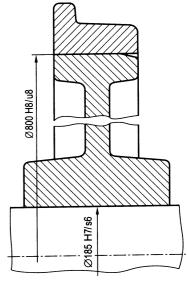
Крепление бандажа на центре колеса и центра колеса на валу
